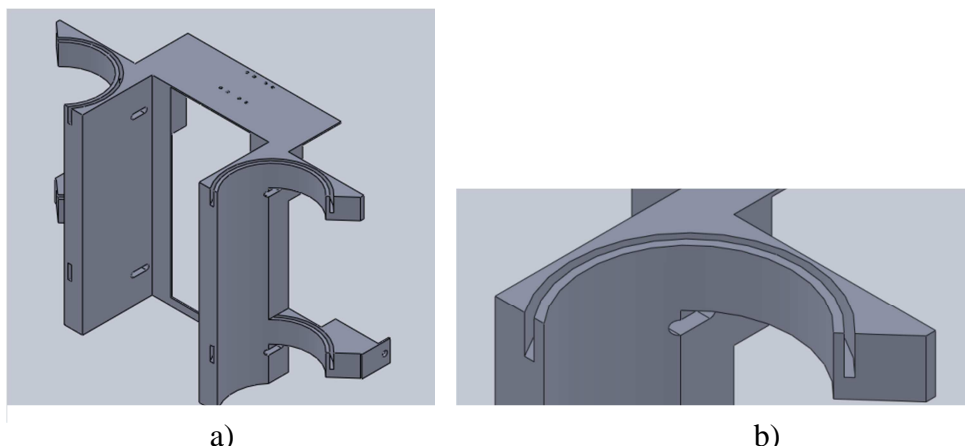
Detalle de la separación entre la pila y la estructura principal
